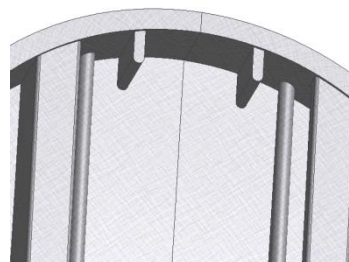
Mechanismus spojující technický díl se vzhledovým dílem.
